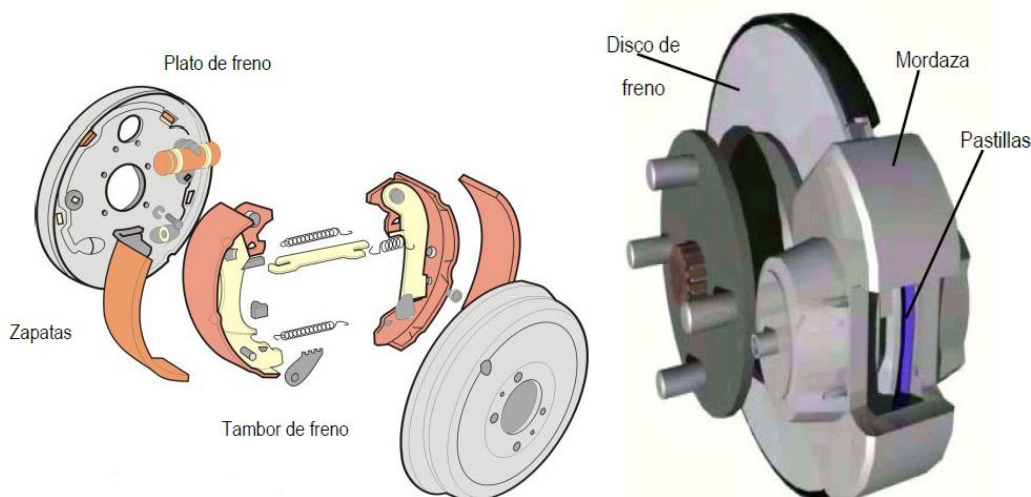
Tipos de freno. De izquierda a derecha: de tambor y de disco.
